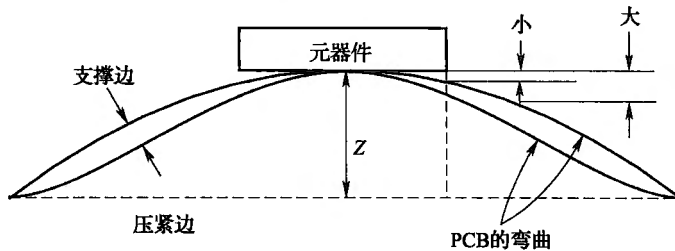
器件与支撑边 PCB 和压紧边 PCB 之间相对运动的差异
